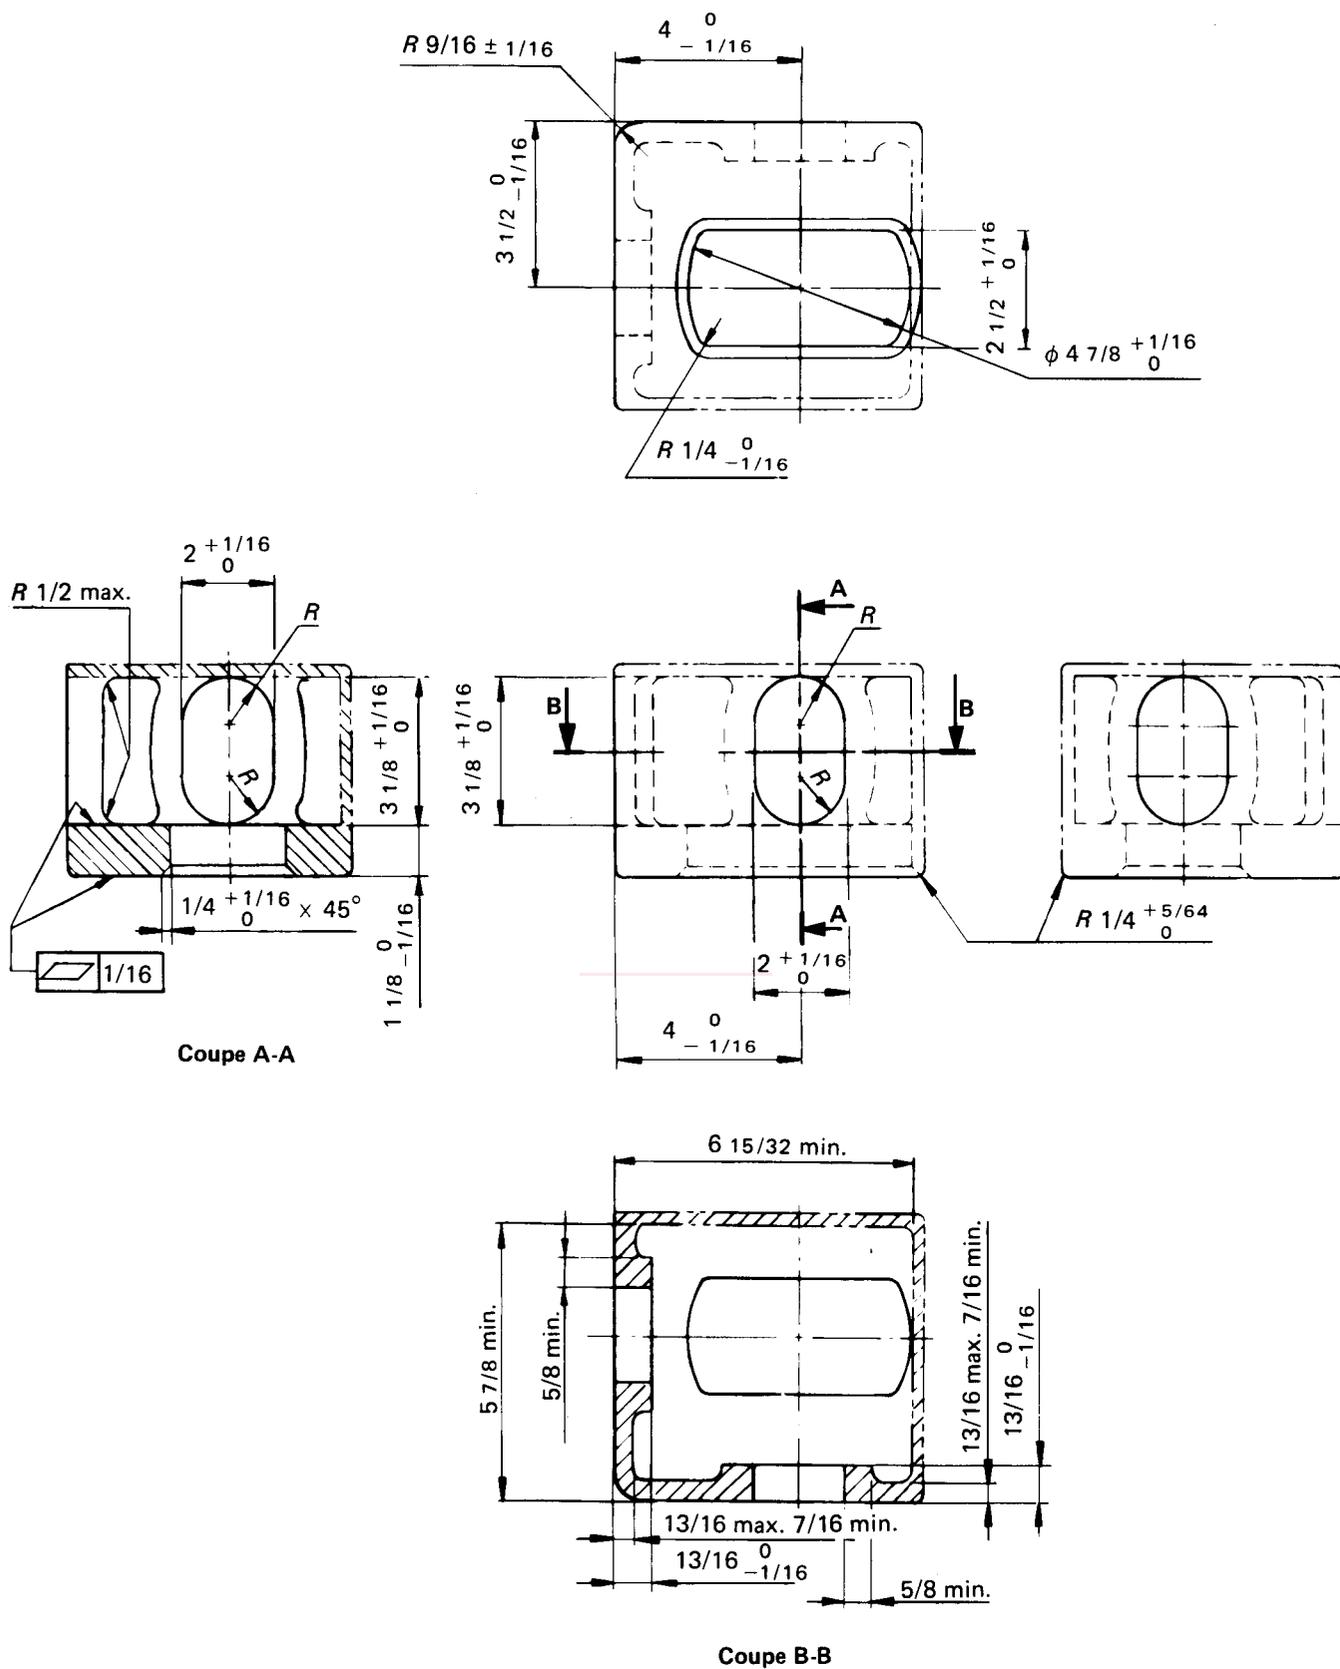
Pièce de coin supérieure — Dimensions en millimètres
